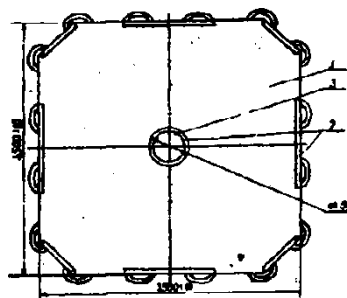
Пневматическое прыжковое спасательное устройство: 1 – пневматическая камера; 2 – надувной каркас; 3 – сетка; 4 – отверстия; 5 – вентиль; 6 – предохранительный клапан; 7 – штуцер; 8 – ручки; 9 – круг; 10 – метка.
